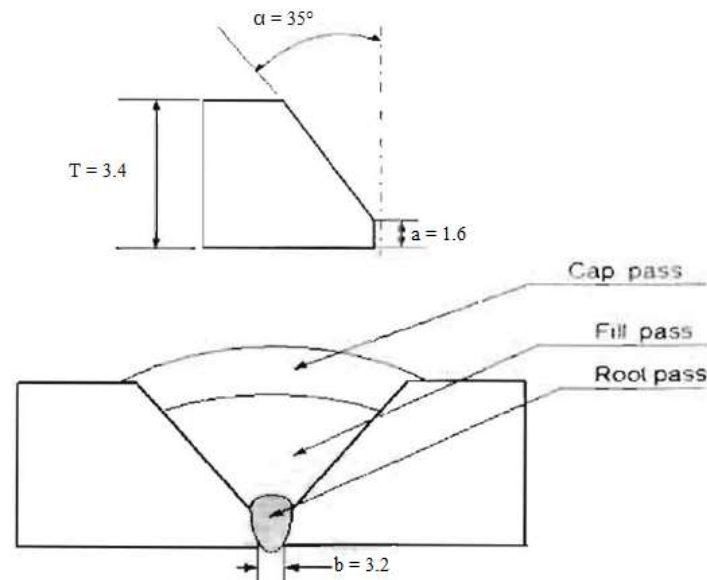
Forme du joint de soudure et le nombre de passe.
